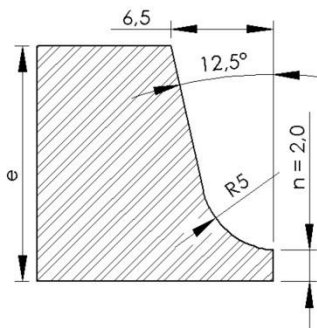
Chanfro tipo “U” utilizado por Pigozzo [16] para a execução de procedimentos de soldagem TIG mecanizada. Dimensões em mm.
